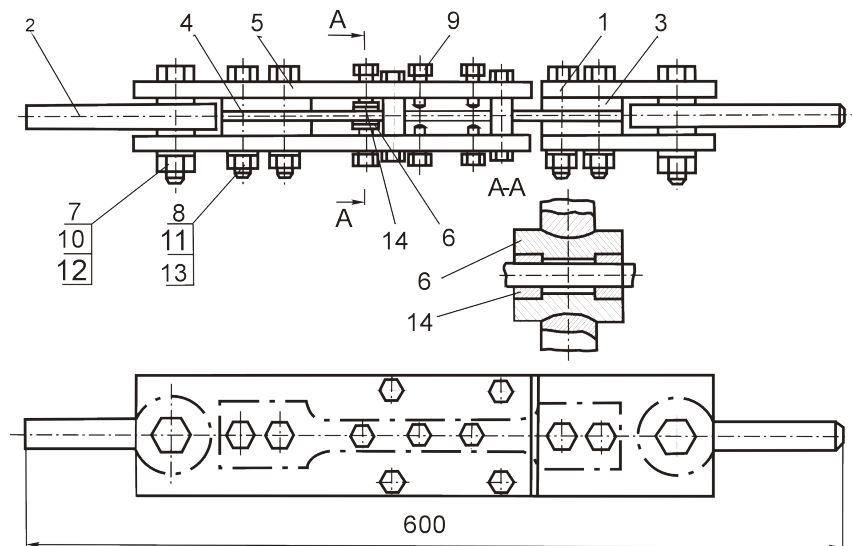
Приспособление для исследования влияния амплитуды относительных перемещений на усталостную долговечность гладкой полосы в условиях фреттинг-коррозии: 1 – пластина; 2 – проушина - захват; 3 – прокладка; 4 – образец гладкой полосы; 5 – накладка приспособления; 6 – прижим; 7 – 13 – крепежные детали; 14 – шайба
